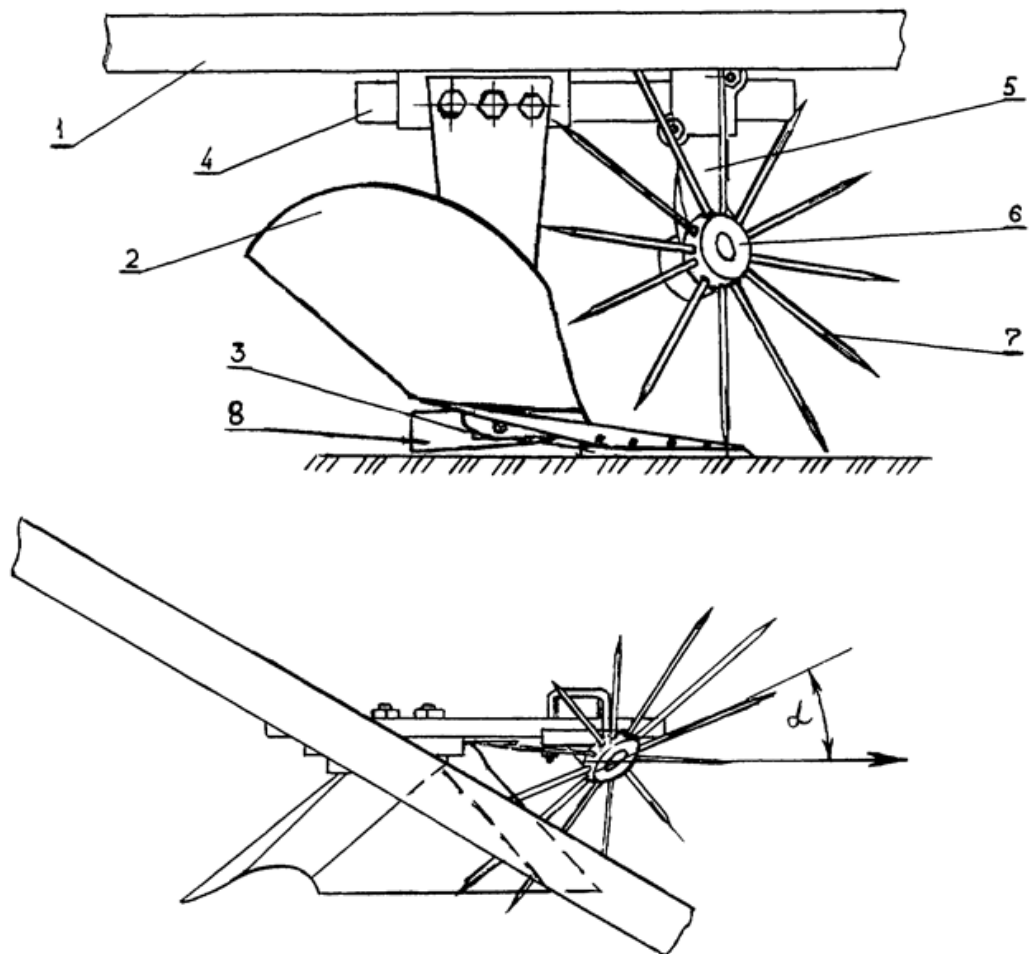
Корпус з голчатим передплужником: 1 – рама; 2 – відвал; 3 – леміш; 4 – державка; 5 – стійка; 6 – маточина; 7 – розпушувальні голки; 8 – польова дошка.
